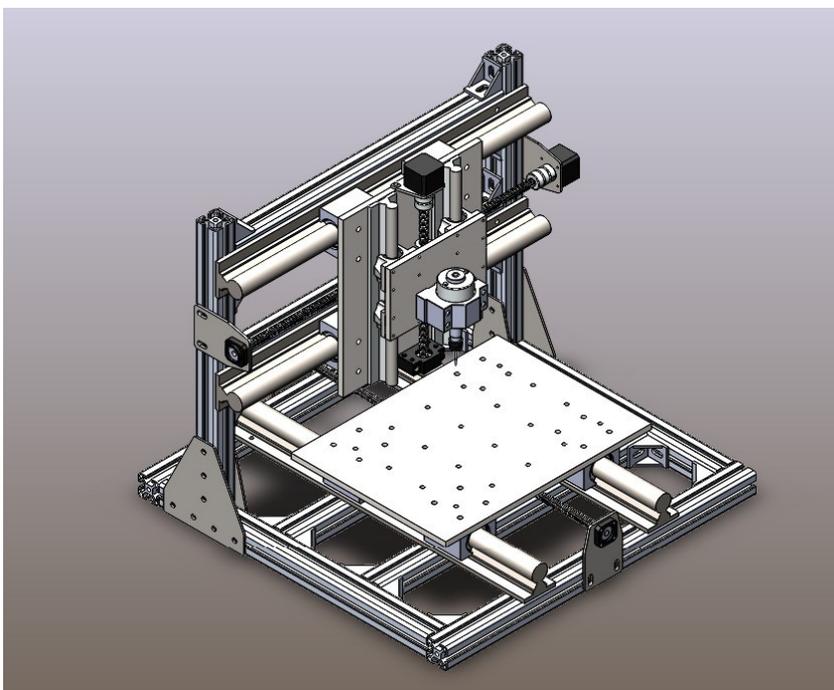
Модель фрезерного трехкоординатного портального станка с ЧПУ.
